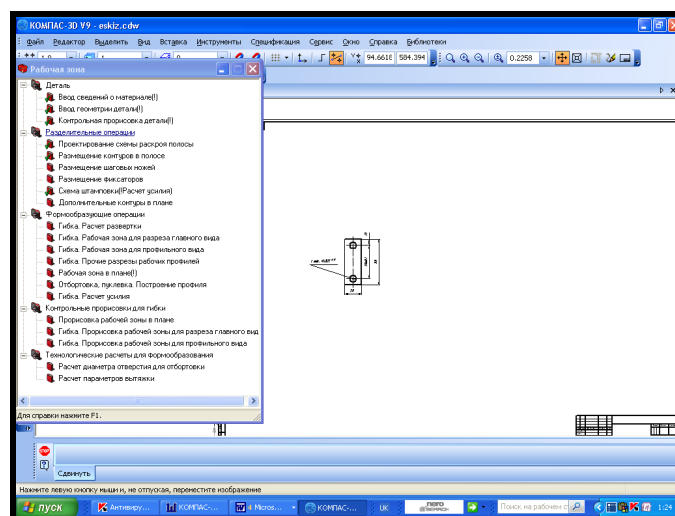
Фрагмент креслення деталі "Планка".
